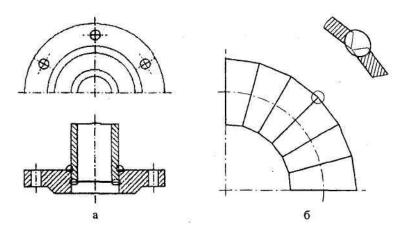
Поперечные сечения сварных соединений а – штуцера и фланца, б – сборного колена
